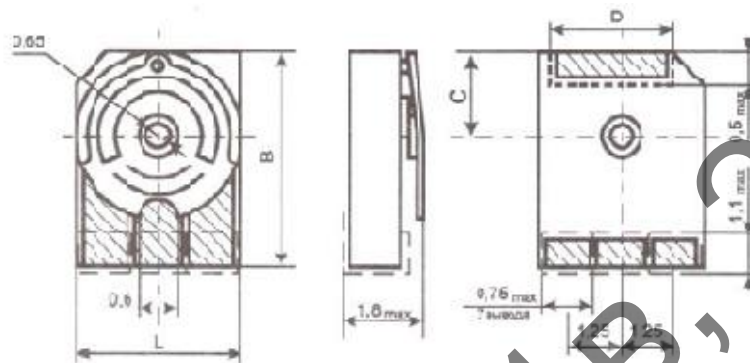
Зовнішній вигляд підстроювального резистора РП1-75
